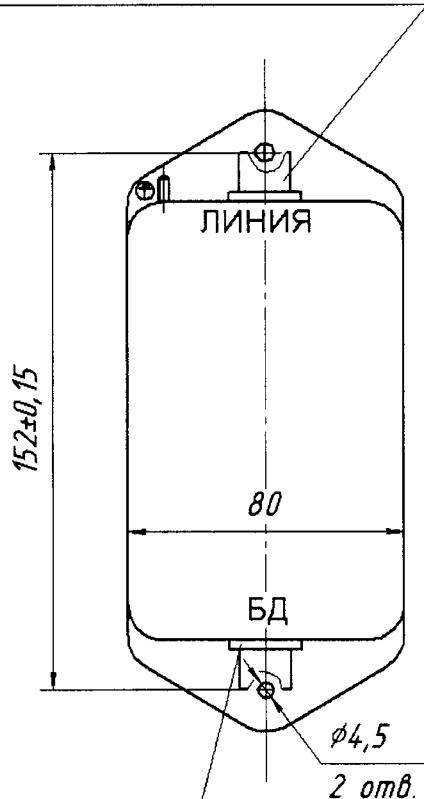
Габаритные и присоединительные размеры блока БСПП-16д
